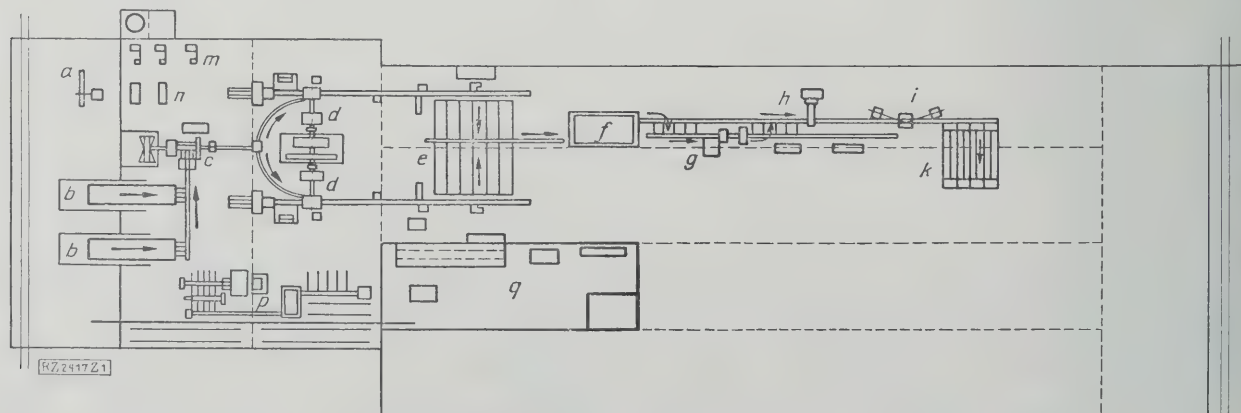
Rohrwalzwerkanlage der Pittsburgh Steel Products Co., Allentown, geliefert von der Demag, Duisburg, Lageplan
